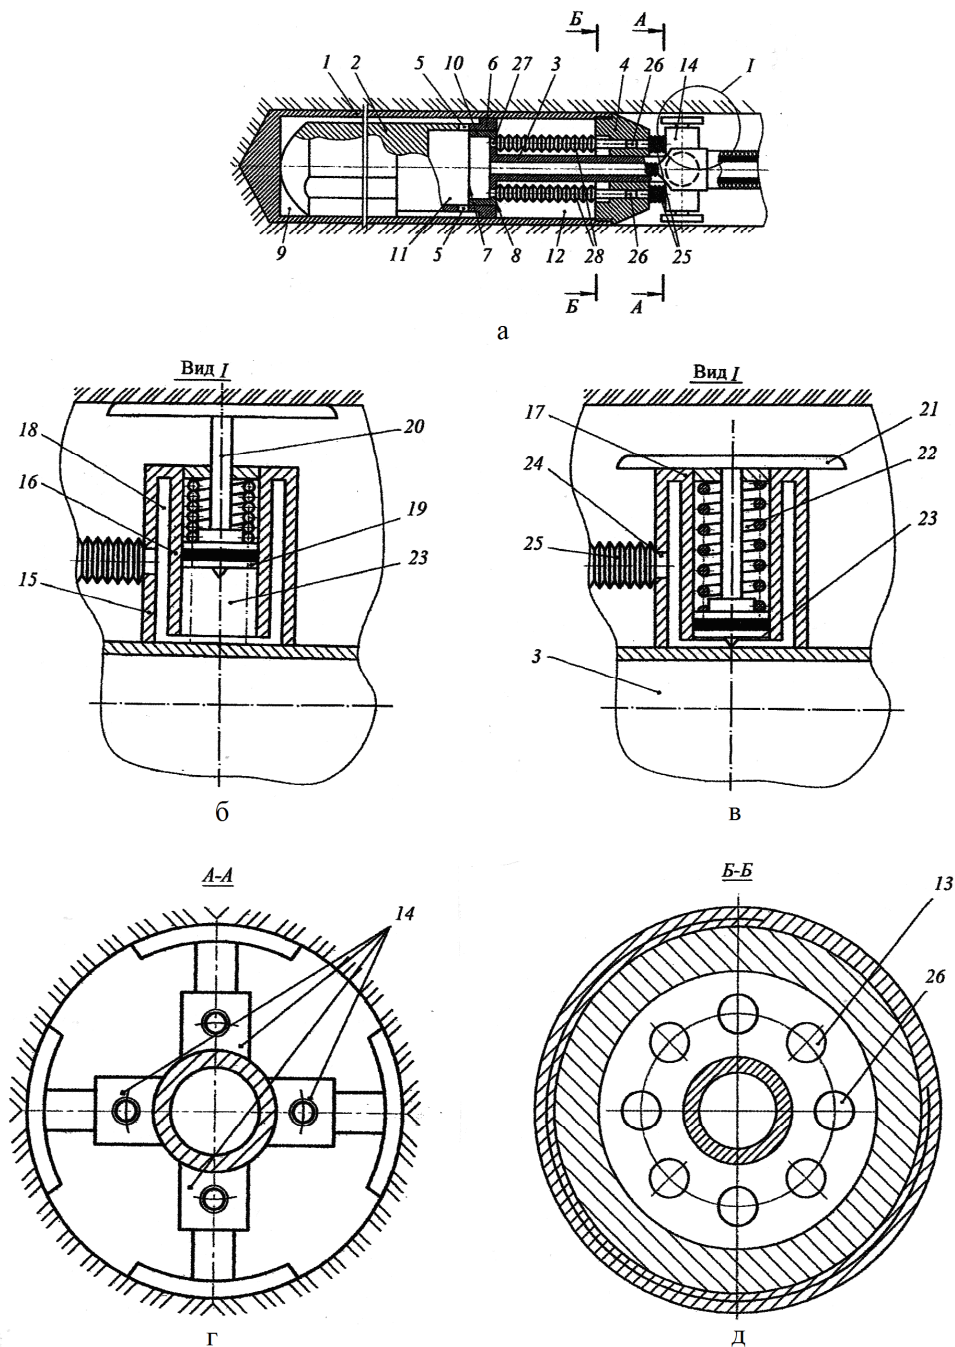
Самодвижущийся пневмопробойник с пневматической системой управления стопорным механизмом: а – принципиальная схема; б – положение стопорного механизма при разгоне ударника; в – положение стопорного механизма при выходе пневмопробойника из скважины; г – сечение А-А; д – сечение Б-Б; 1 – корпус; 2 – ступенчатый ударник; 3 – патрубок; 4 – гайка; 5 – окна; 6 – направляющий пояс; 7, 8 – воздухораспределительные кромки; 9 – рабочая камера холостого хода; 10 – передняя ступень патрубка; 11 – камера рабочего хода; 12 – камера отвода отработавшего воздуха; 13 – каналы; 14 – стопорные механизмы; 15 – внешний стакан; 16 – внутренний стакан; 17 – основание стаканов; 18 – кольцевая полость; 19 – поршень; 20 – шток; 21 – тормозные башмаки; 22 – пружина; 23 – камера; 24 – отверстие; 25, 28 – сильфоны; 26 – сквозные каналы; 27 – отверстия
